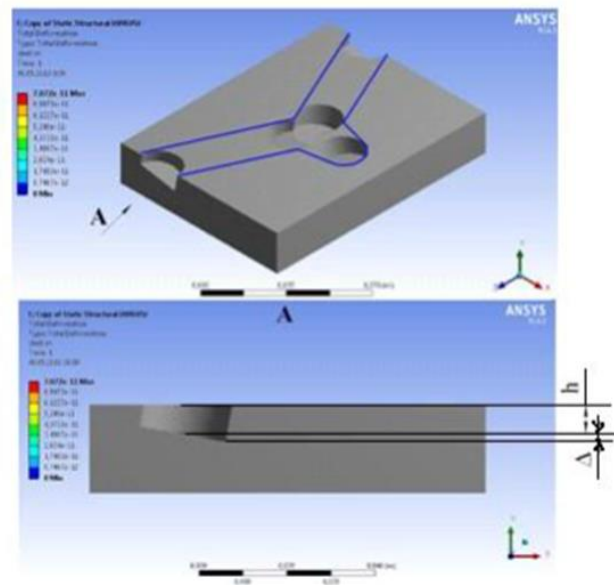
Сечение заготовки в местах, занимаемых оправкой в процессе фрезерования паза
